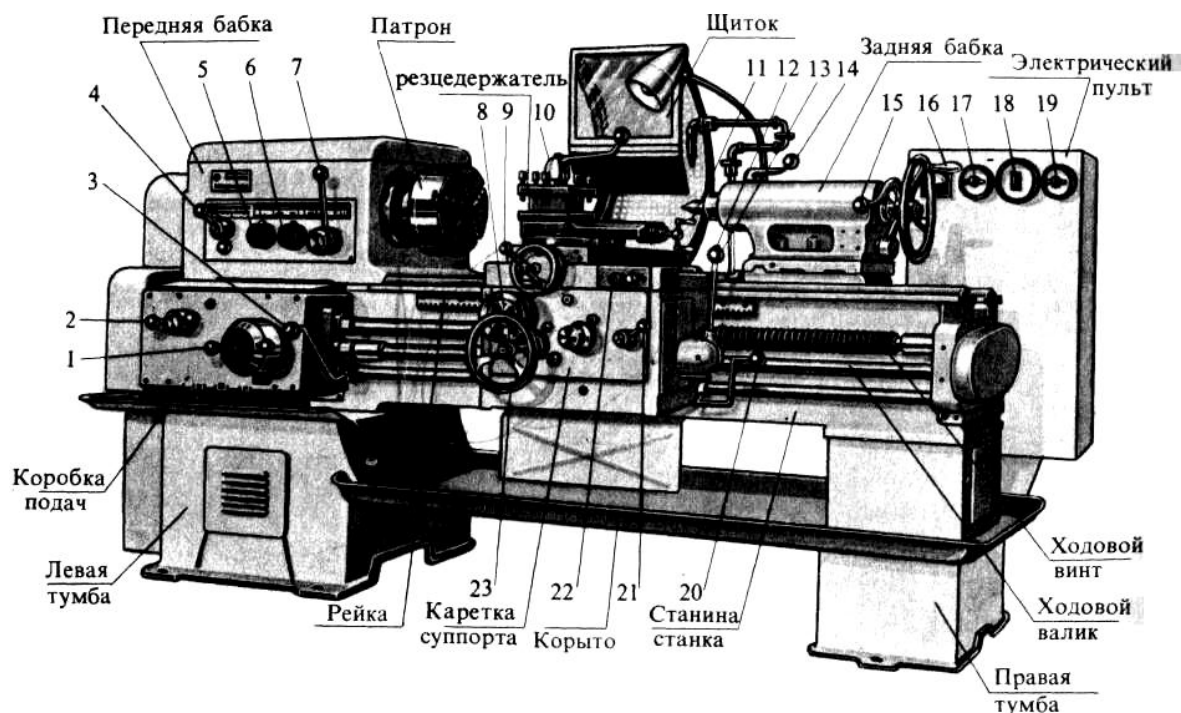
Токарно-винторезный станок модели 1K62
